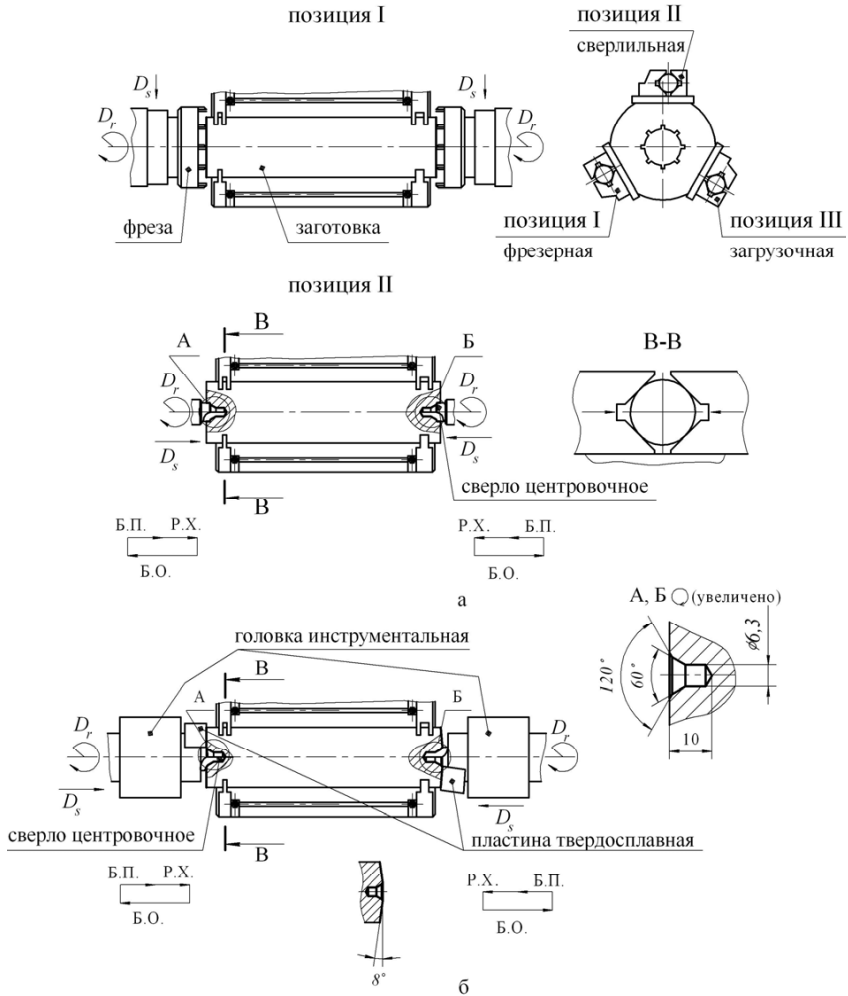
Схема обработки центровых отверстий и торцов на центровально-фрезерном (а) и центровально-подрезном (б) станках: РХ – рабочий ход; БП – быстрый подвод; БО – быстрый отвод
